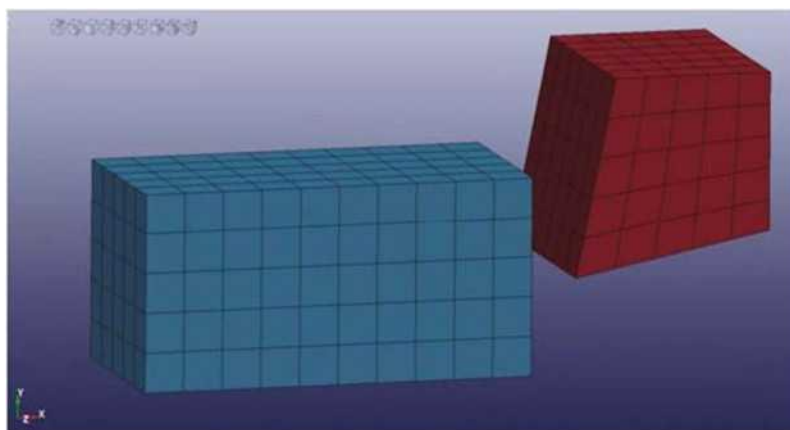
Готова скінченно-елементна модель заготовки та інструменту
